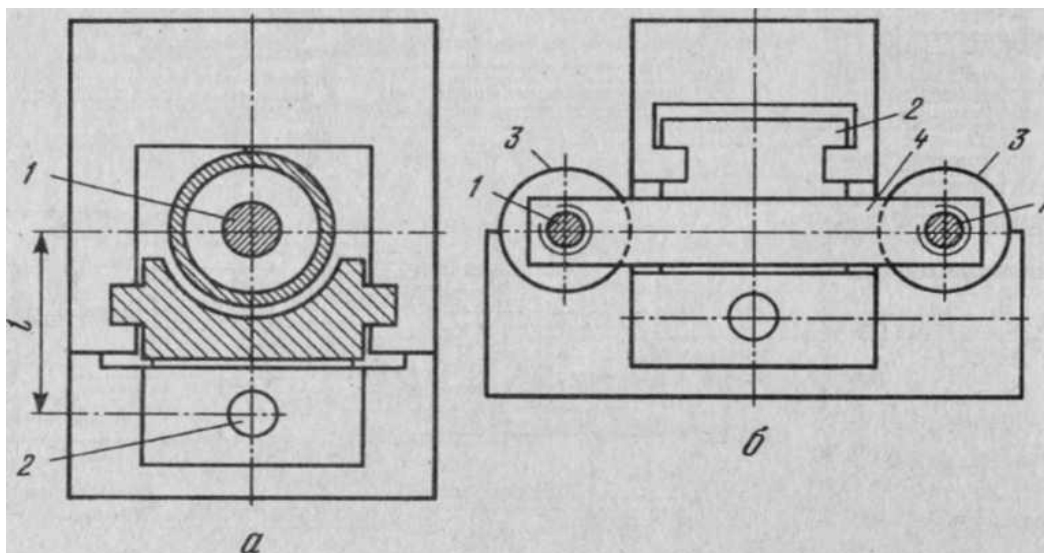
Схемы компоновки вертикально-протяжных станков с одним (а) и двумя (б) тянущими гидроцилиндрами.
